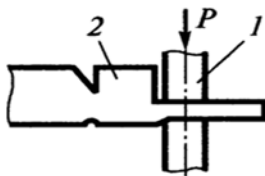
Схема обработки металлов давлением способом свободной ковки
